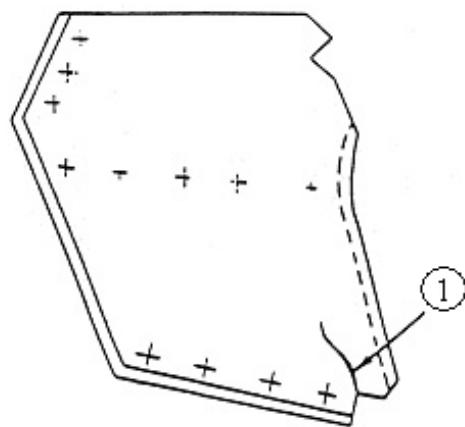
Дефект щита подножки, ремонтируемый сваркой
